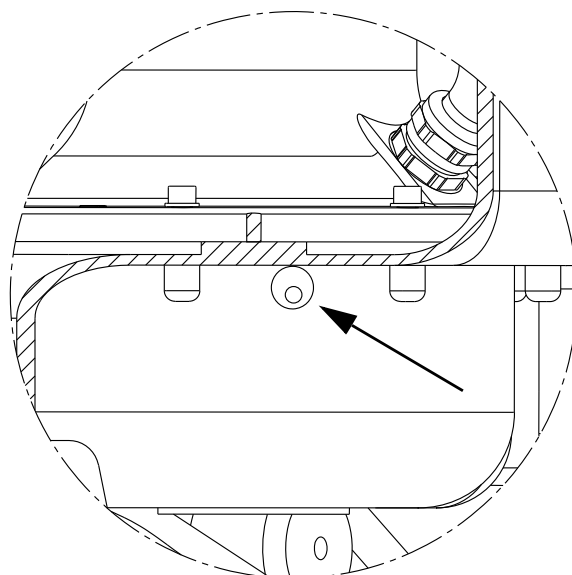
Вентиляционные отверстия в корпусе насоса и сборном резервуаре
